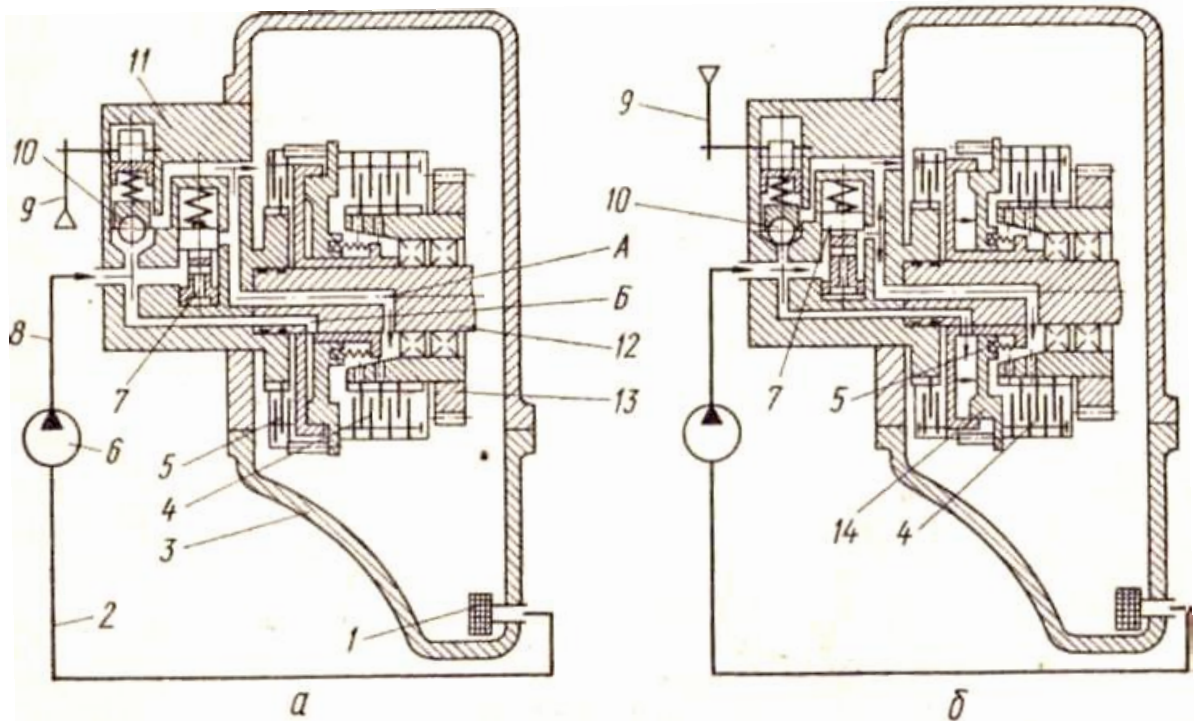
Схема гідросистеми редуктора ВВП:
